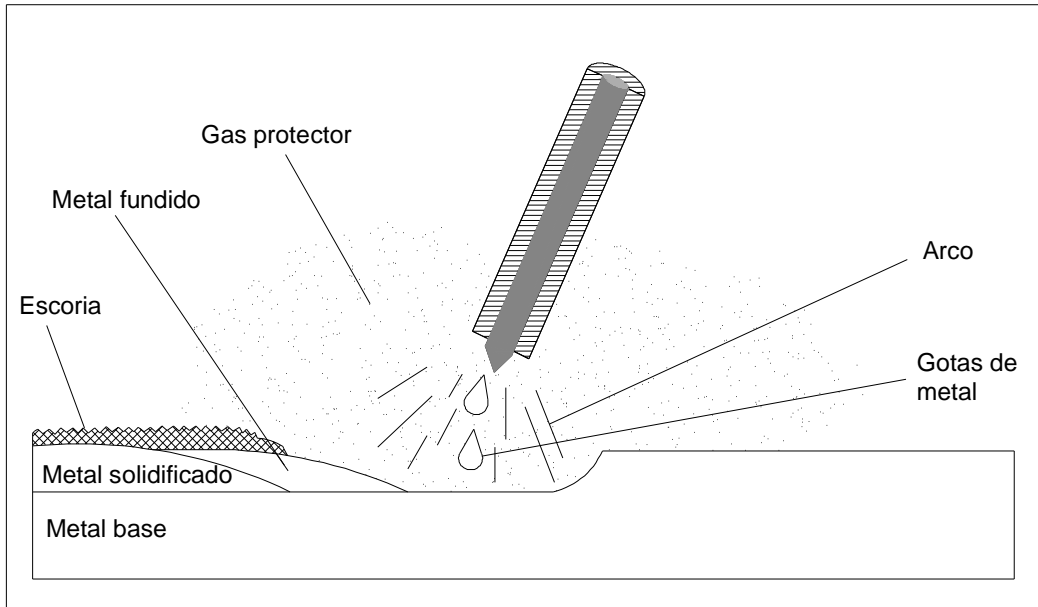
b). - Detalle 1 de la figura N° 13 a) Acción del proceso SMAW en una unión a tope (Manual indura_ soldadura, Pág. 25).
